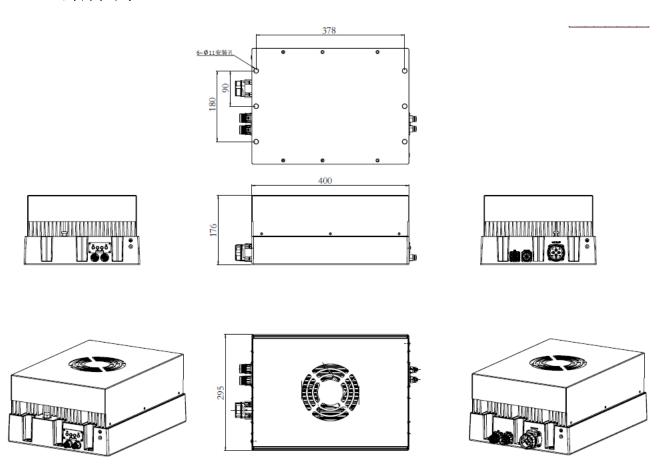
GTR25 高防护共母线整流器外形尺寸图
